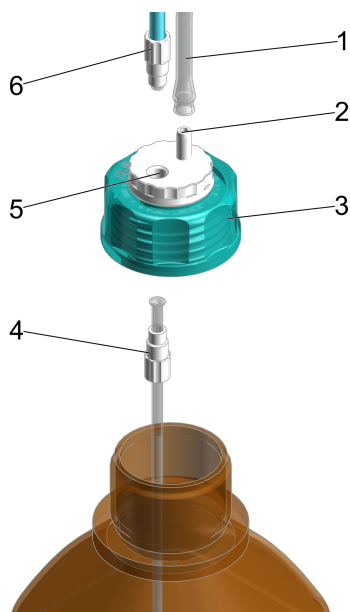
Bestücken des Siphon Breaker für die Reagenzflasche (Solvent)
